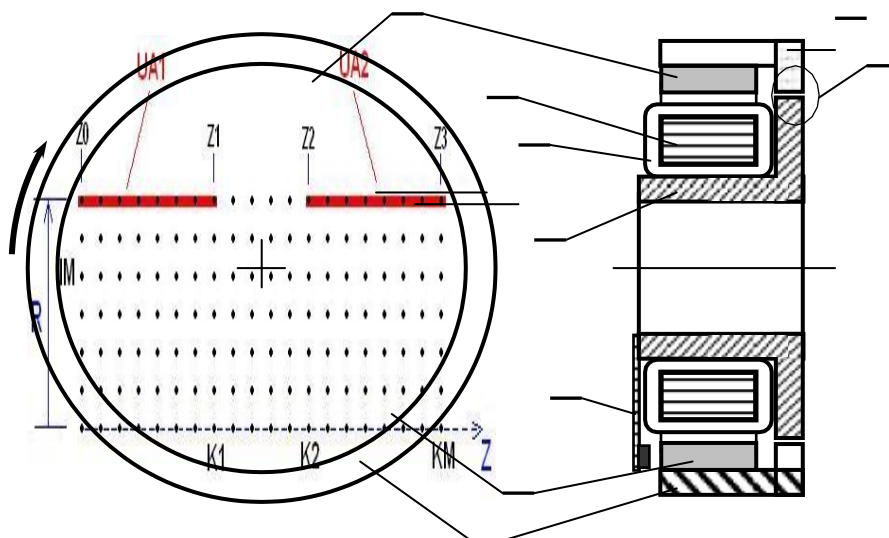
Вентильный двигатель постоянного тока (обращенной конструкции)
